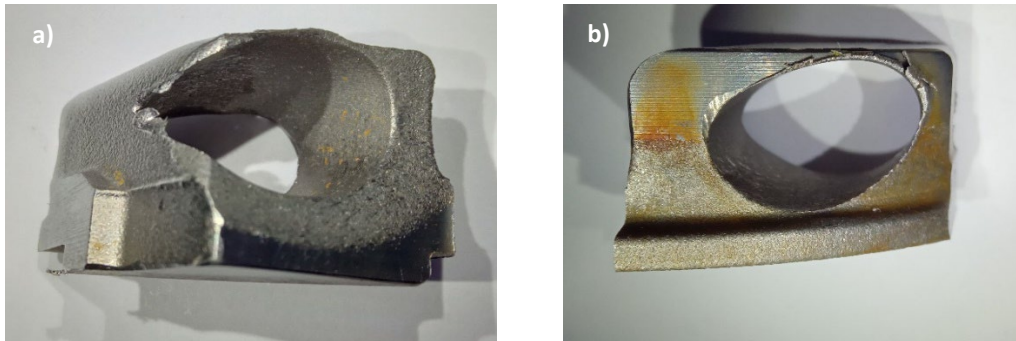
Eje del asiento a) Lado Izquierdo b) Lado Derecho
